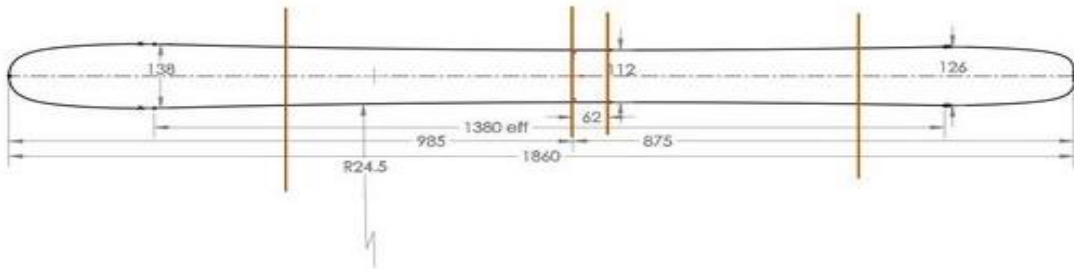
Disseny de la planta d'un esquí amb SolidWorks (Skibuilders)
